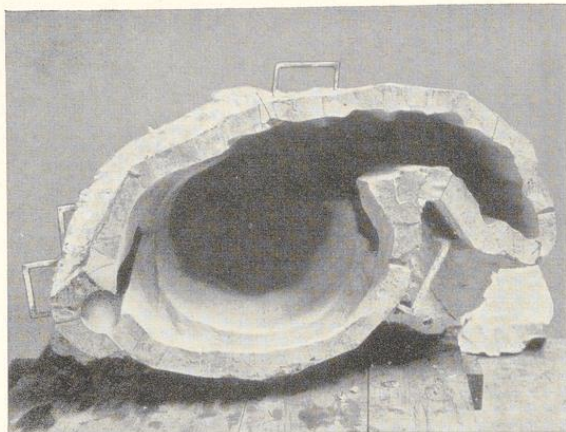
Fertige Formschale zum Ausstampfen mit Kunststeinmasse
